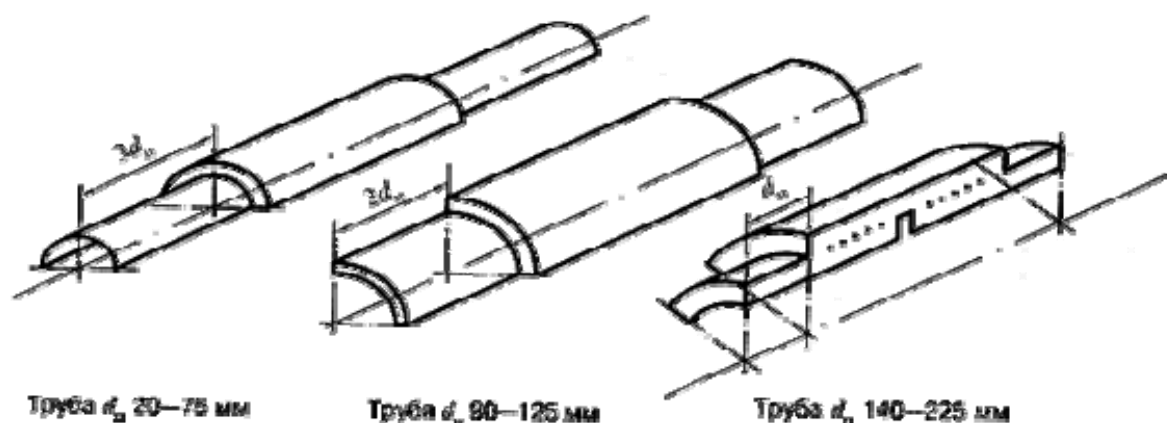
Общий вид полиэтиленовых образцов-сегментов
